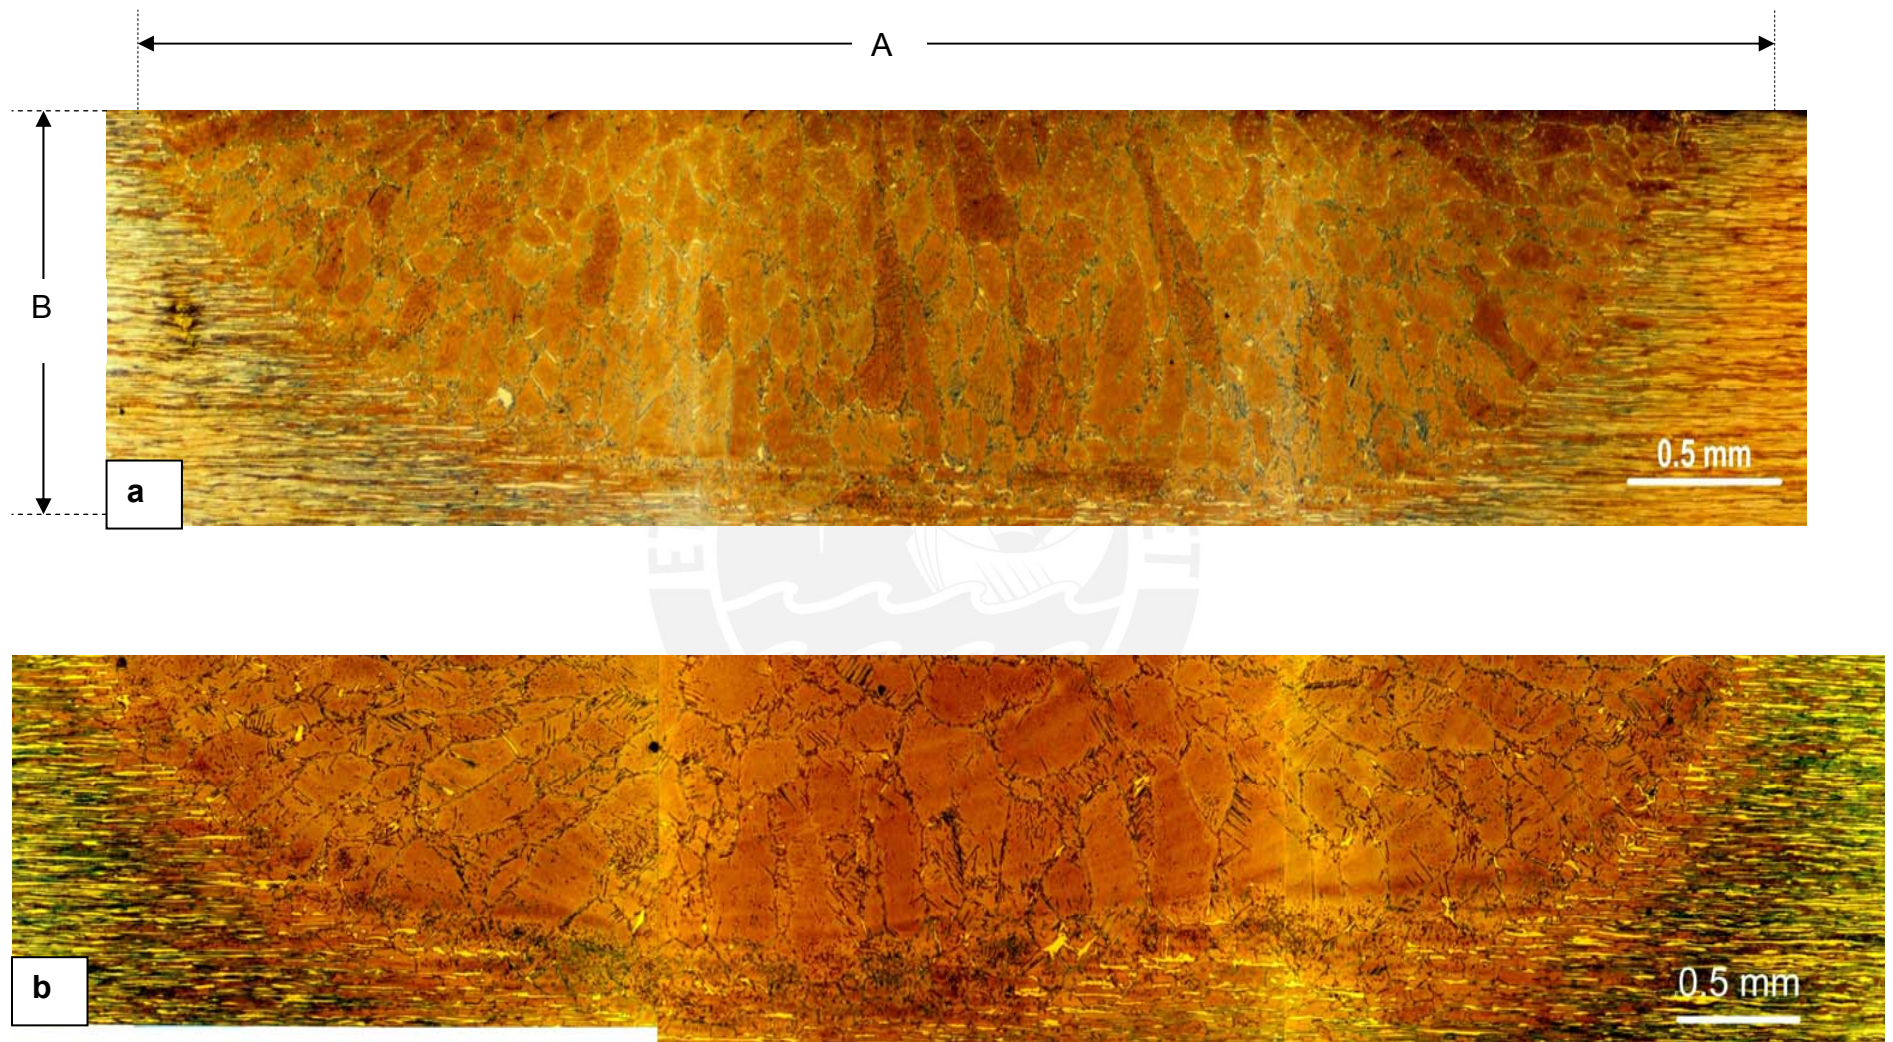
Aspecto macrográfico de los cordones de soldadura para las condiciones .a) 4 kJ/cm - 25°C b) 9 kJ/cm - 25°C
